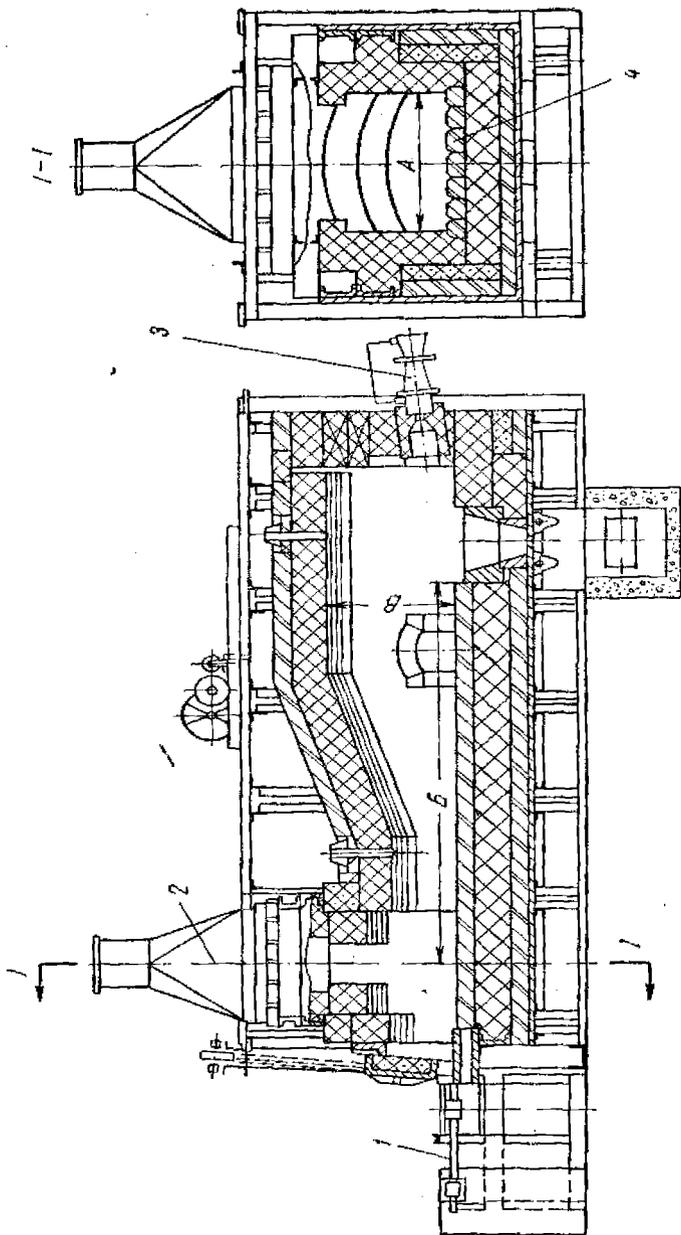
Печь нагревательная методическая (кузнечная) с желобчатым подом с выдачей заготовок через под НУОЖ (НУЗЖ); 1 — загрузочный толкатель; 2 — вытяжной зонг; 3 — горелка; 4 — желобчатый под
